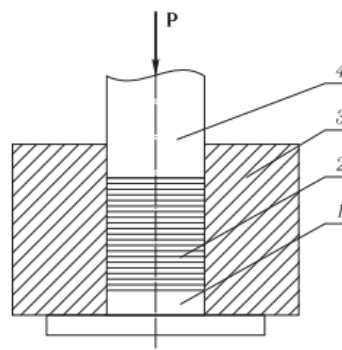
Схема полусухого прессования, 1 – нижний пуансон, 2 – материал, 3 – матрица пресс – формы, 4 – верхний пуансон.
